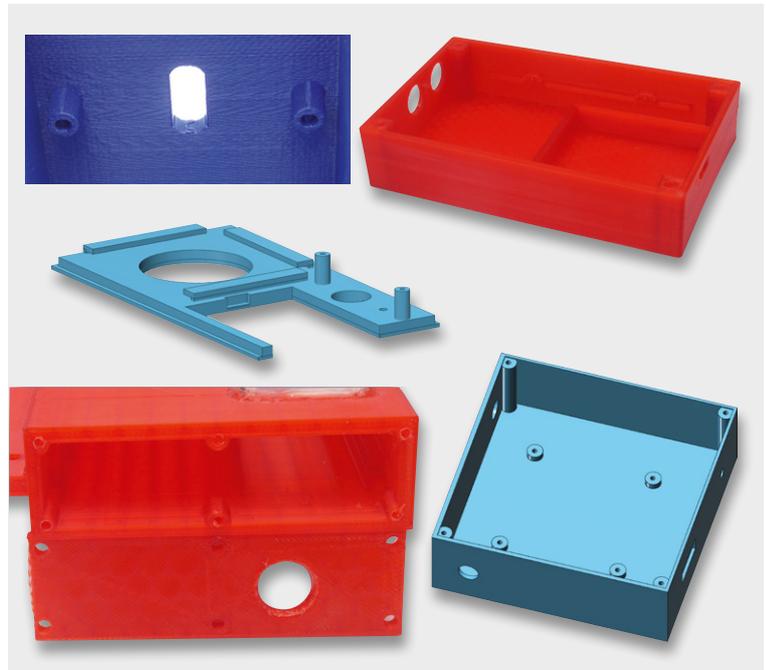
Einkonstruierte Schraubendome mit Schraubenlöchern erleichtern die Montage.
